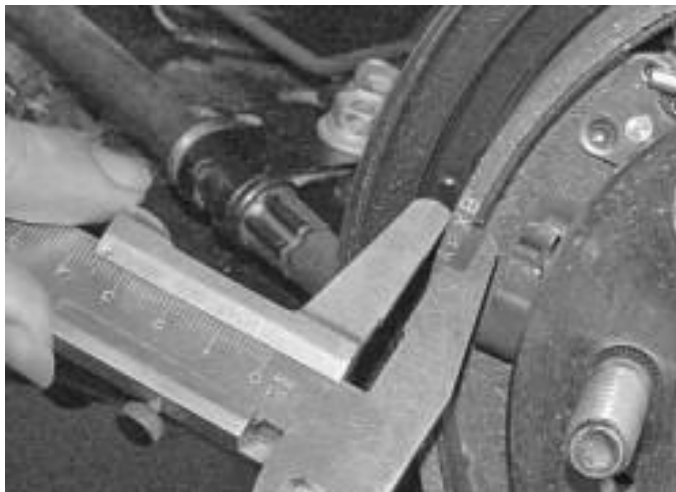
Вимірювання товщини фрикційних накладок штангенциркулем
